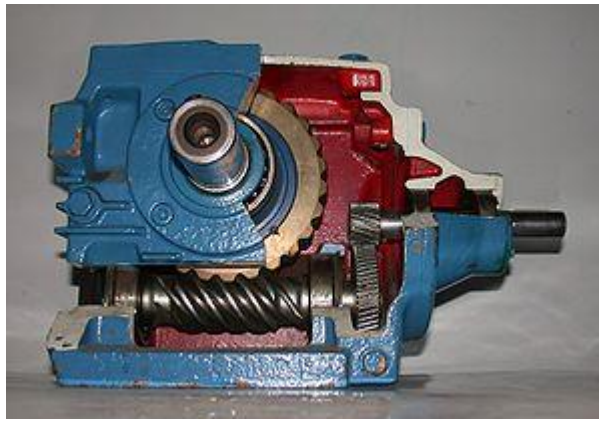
Загальний вигляд комбінованого черв'ячно-циліндричного редуктора
